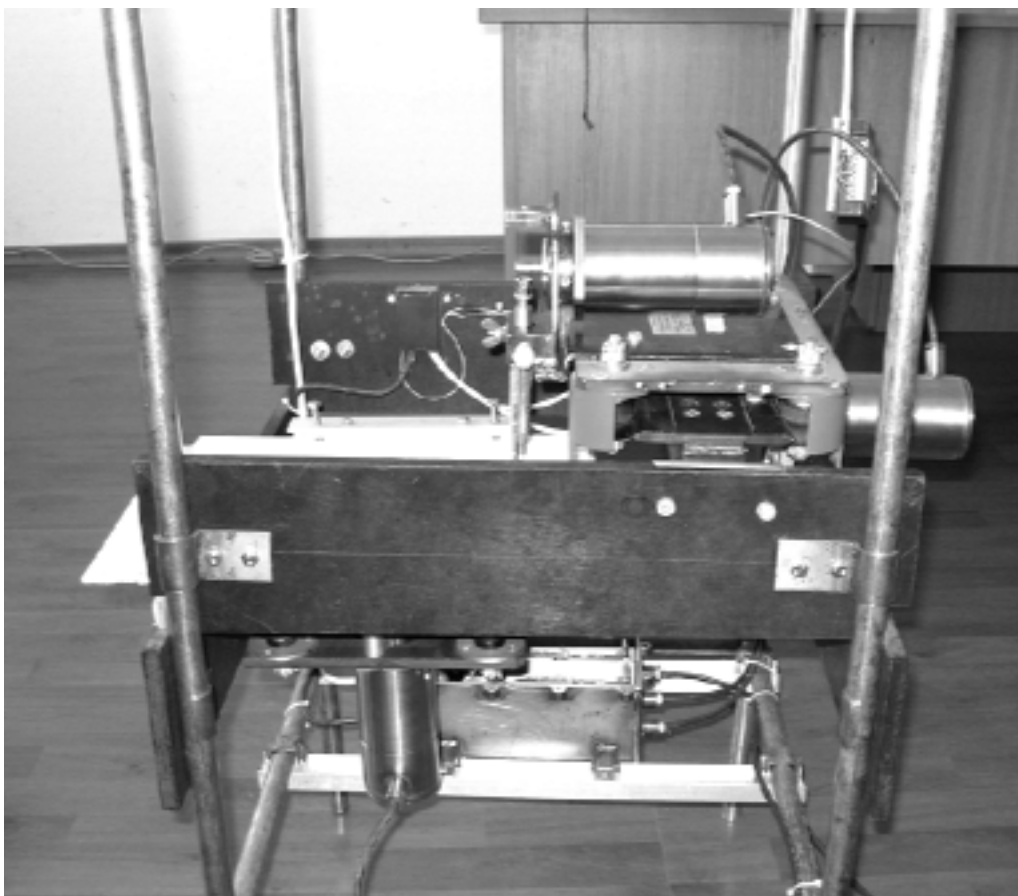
Рабочий макет автомата для сварки и резки в водной среде
